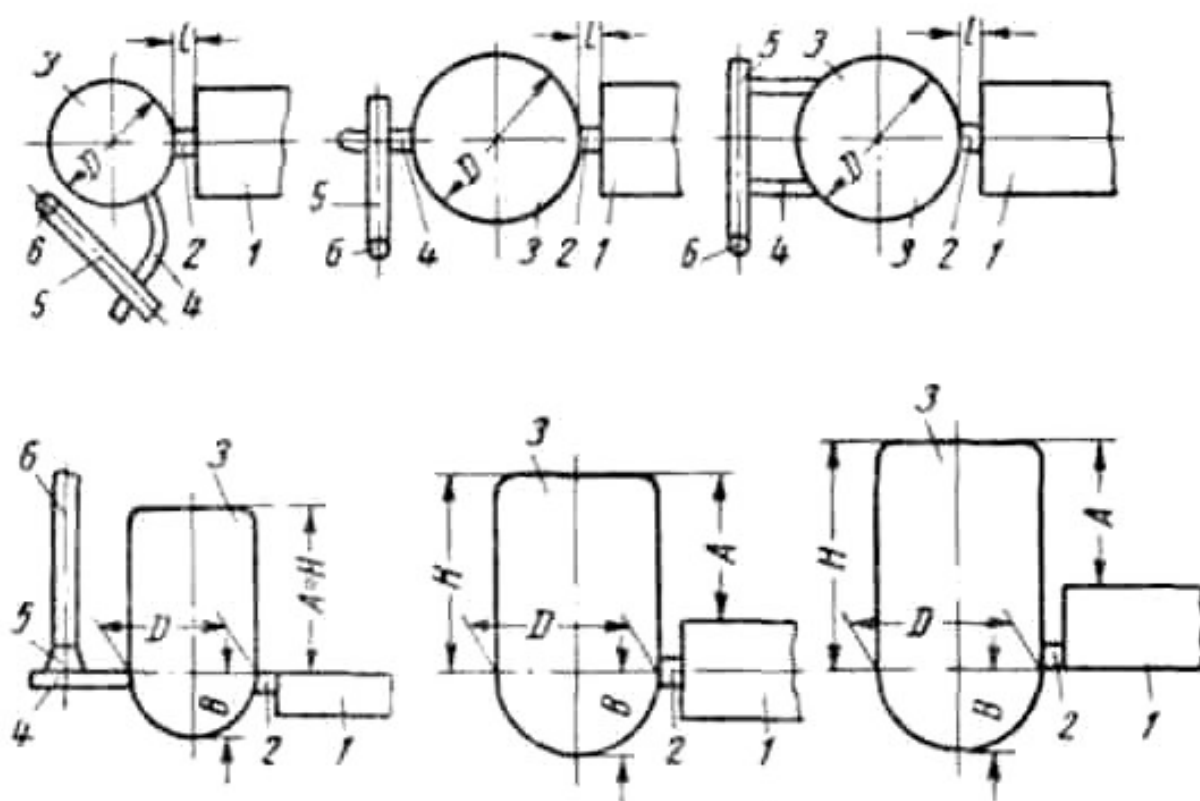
Питающие бобышки из ковкого чугуна: 1 — стояк; 2 — шлакоуловитель 3 — питатель; 4 — бобышка; 5 — шейка; 6 — отливка
